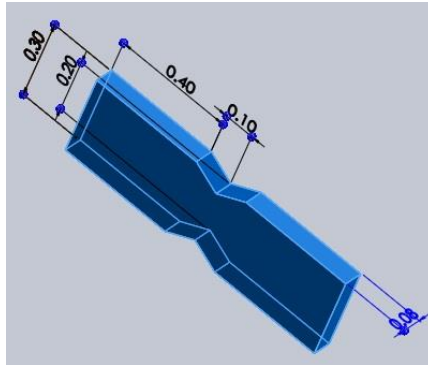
Modelado de la pieza fabricada en la impresora 3D con el material compuesto utilizada para tensión (unidades pulgadas). Fuente: TecNM / ITN.
